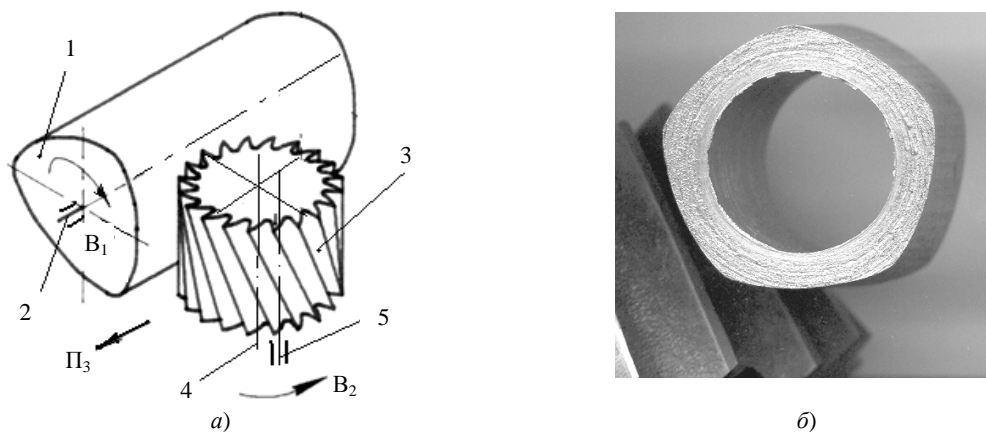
Кинематическая схема обработки некруглой поверхности (а), образец детали с некруглой поверхностью и фрагмент режущей части инструмента (б)
